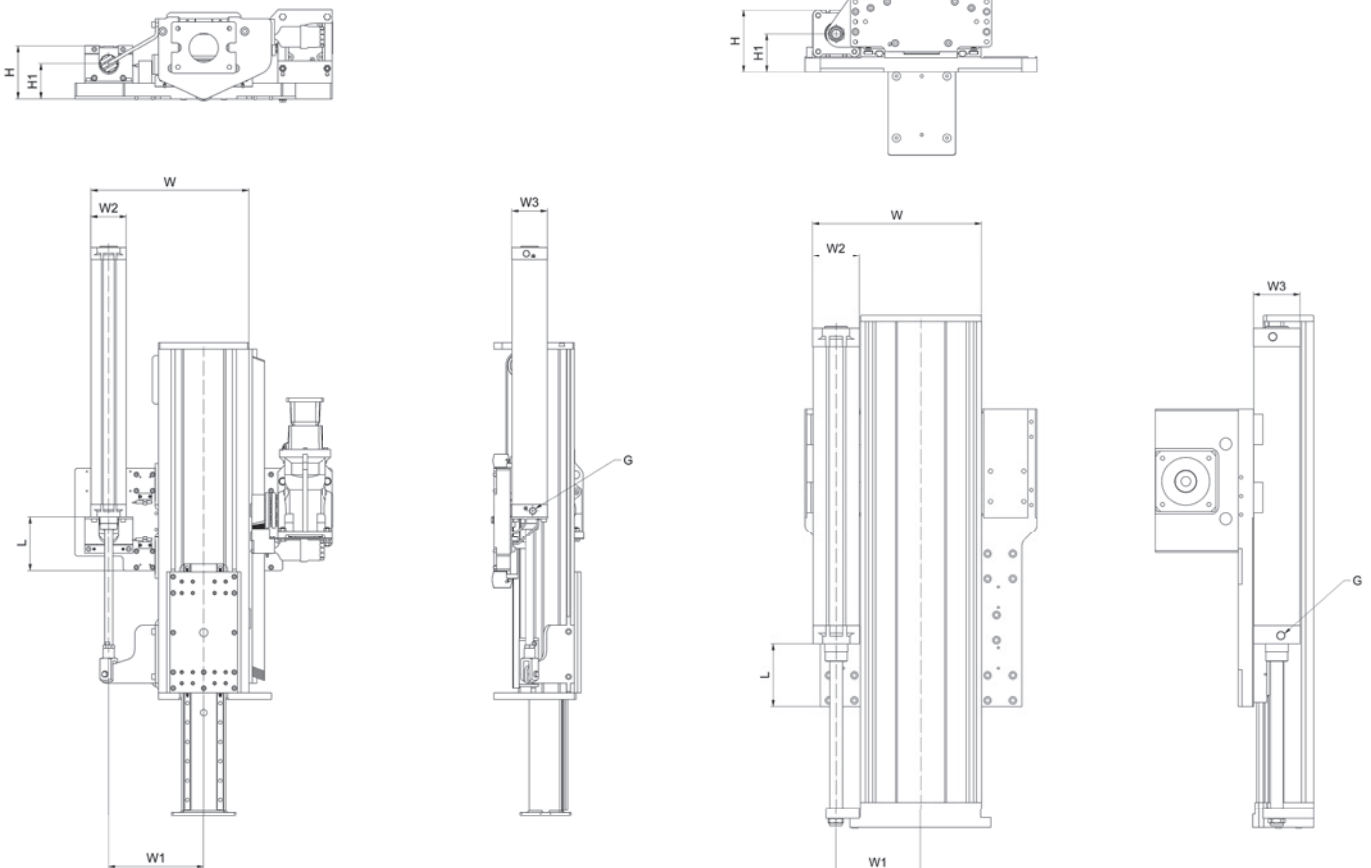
AXDL240A und AXS280TV mit Ausgleichszylinder
